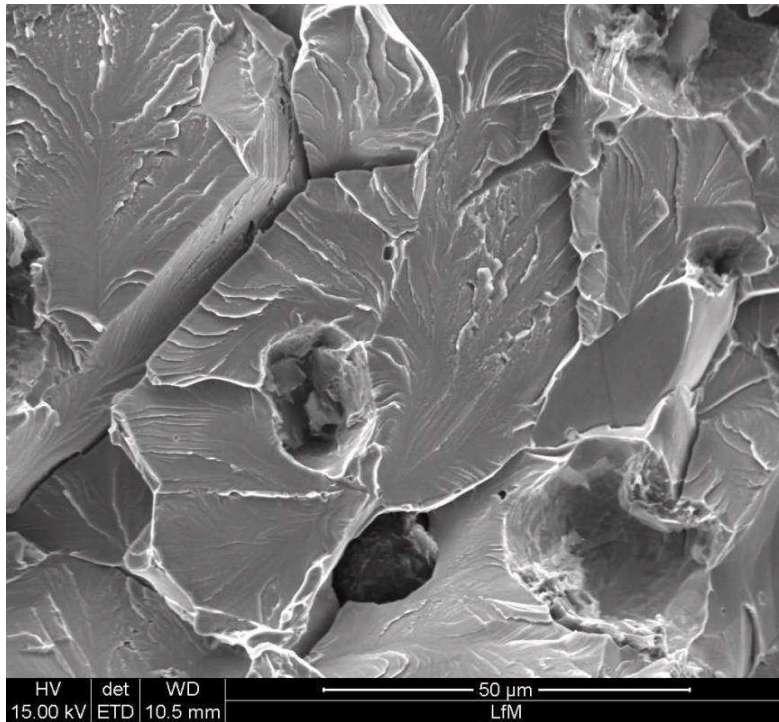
Genauere Betrachtung, Sprödbruch
